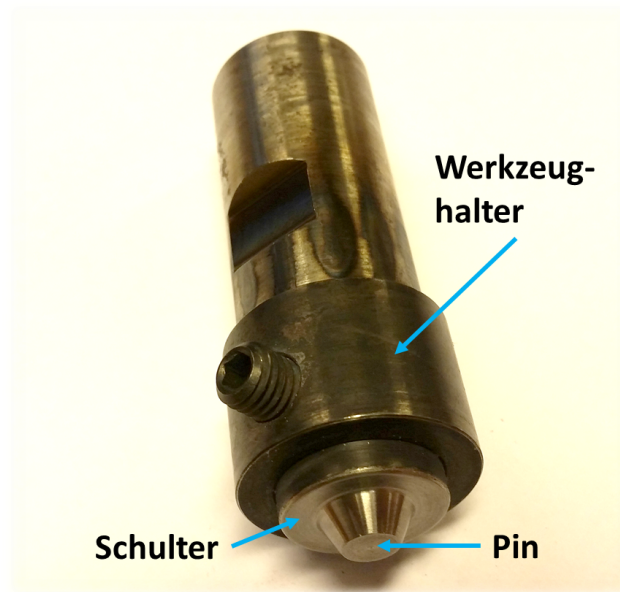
Aufbau eines Werkzeugs, das für das Rührreibschweißen benötigt wird.
